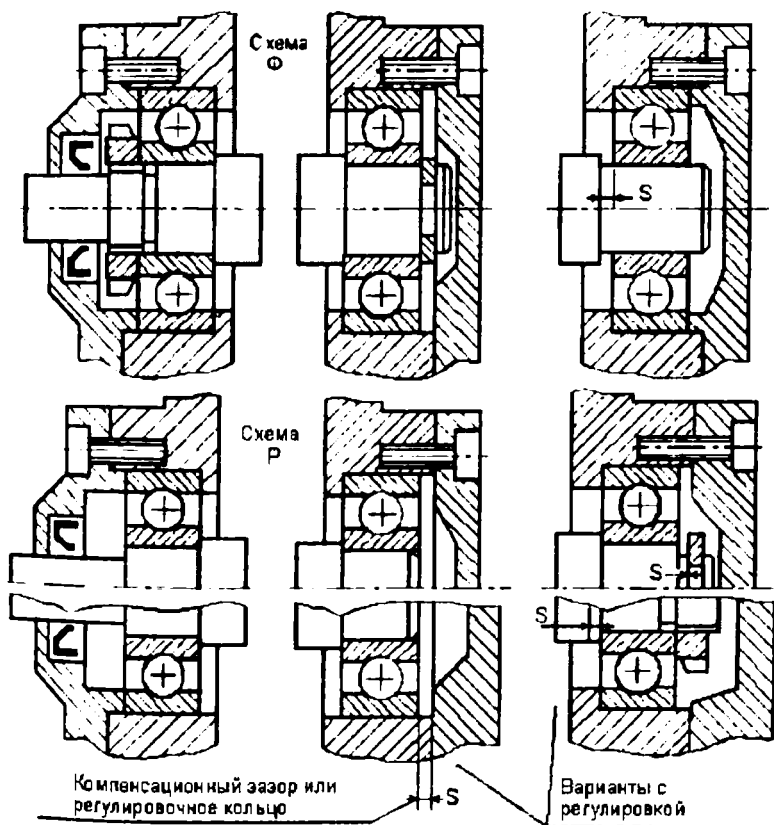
Примеры конструкции опор с различными схемами установки
